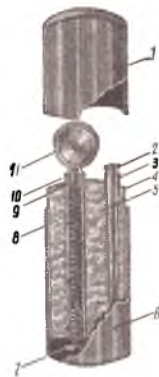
Схема устройства неавтоматической карманной бензо-искровой зажигалки: 1 — крышка-колпачок наружного корпуса; 2 — фитиль; 3 — трубка фитиля; 4 — внутренний корпус; 5 — вата; 6 — нижняя часть наружного корпуса; 7 — регулировочный винт пружины кремня; 8 — пружина кремня; 9 — кремнь; 10 — трубка пружины кремня; 11 — огниво
